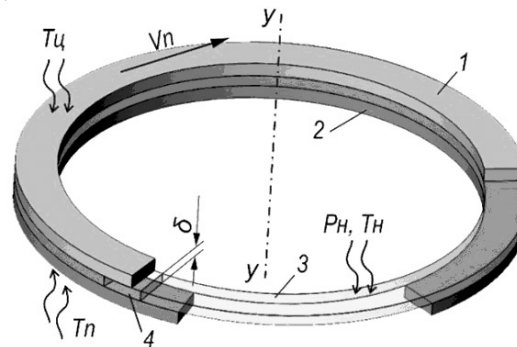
Модель зазора «головка поршня – цилиндр». 1 – подвижное кольцо, 2 – неподвижное кольцо, 3 – газовый зазор, 4 – неподвижный паз.
